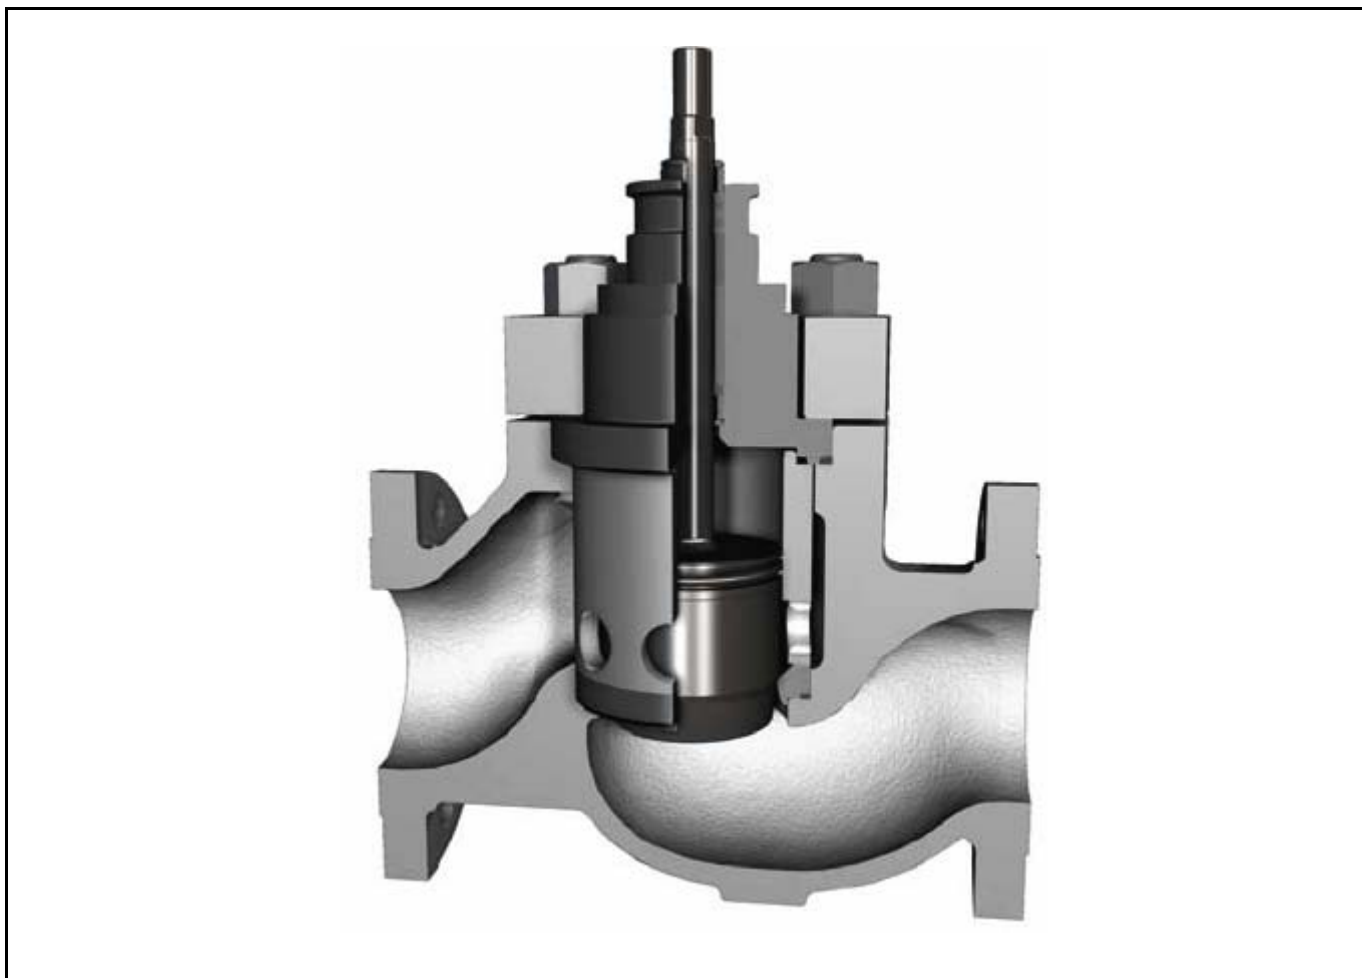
Узел корпуса регулирующего клапана Mark One с разгруженным затвором
